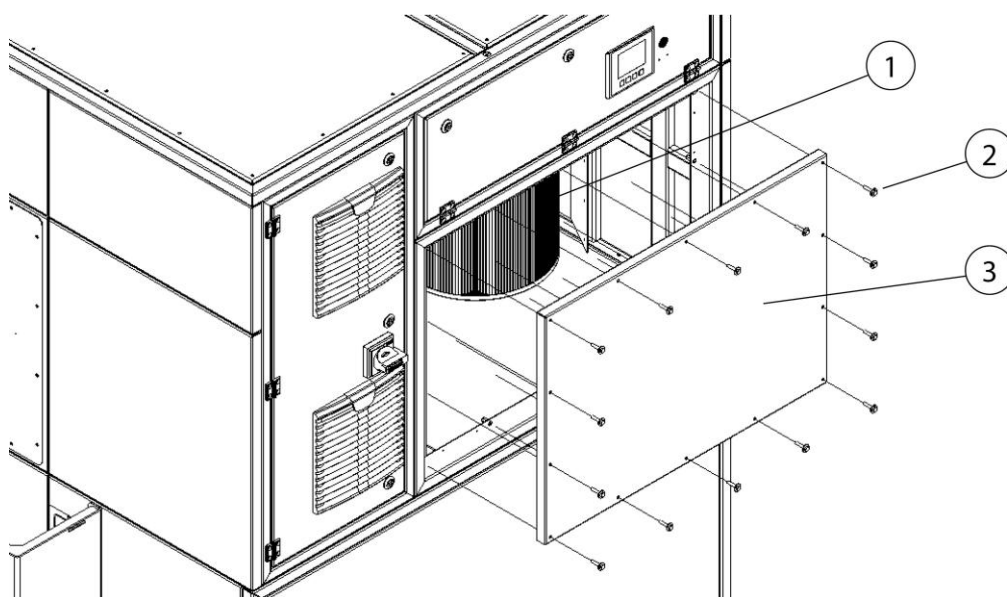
Remplacement du filtre – démontage du couvercle de maintenance
